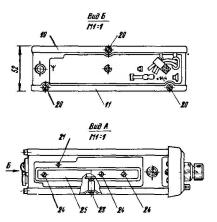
Общий вид автомагнитолы «Звезда 204-стерео» с обозначением расположения узлов и деталей:
